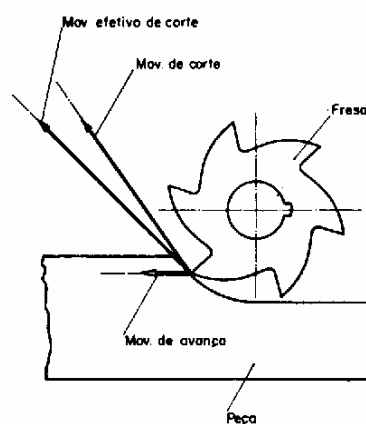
Fresamento com fresa cilíndrica, mostrando os movimentos de corte e avanço.
